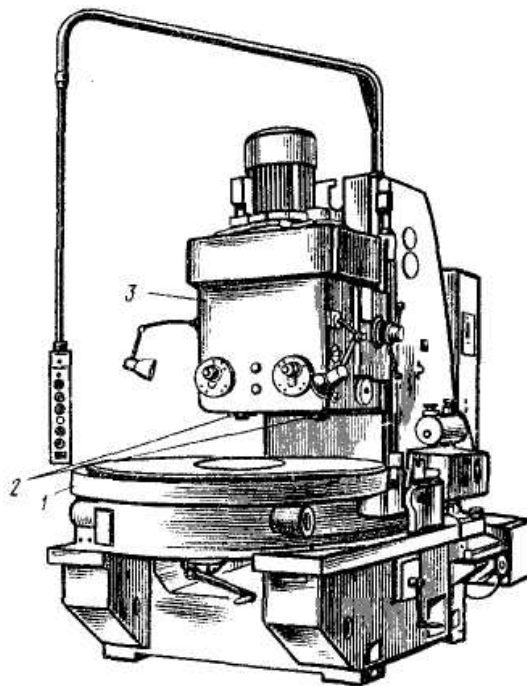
Внешний вид карусельно-фрезерного станка:
